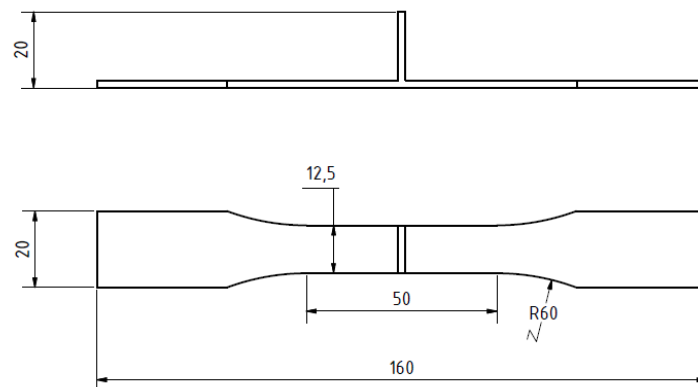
Geometria do provete para ensaio de fadiga (dimensões em mm)
